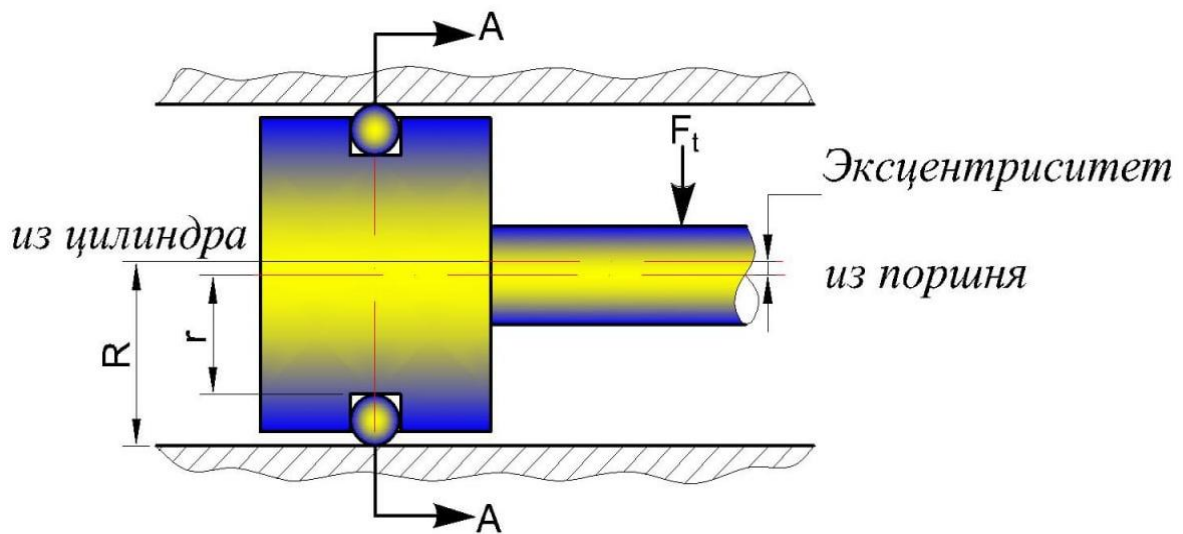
Схема уплотнительного кольца с собранным поршнем.
